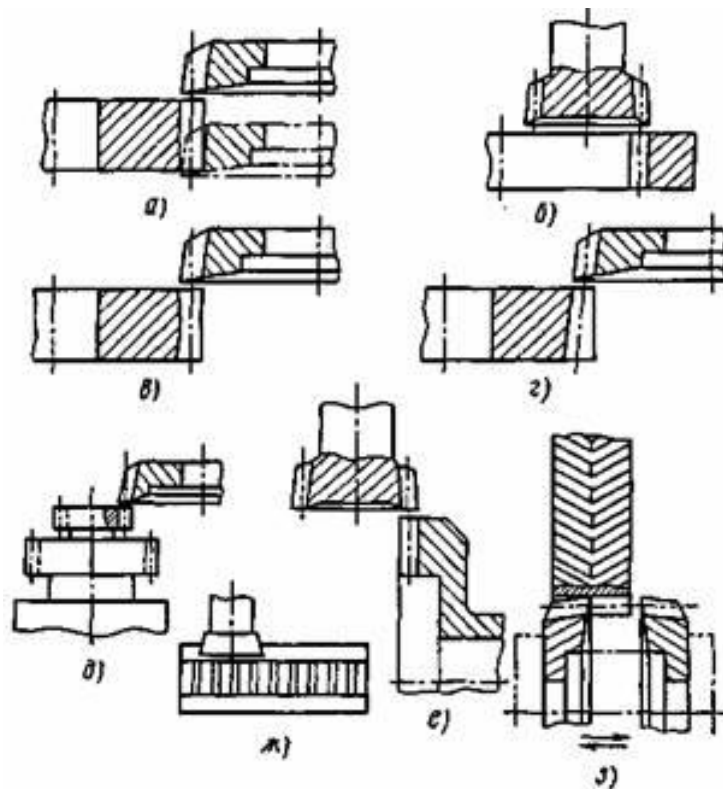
Нарезание зубчатых колес круглыми долбяками на зубодолбежных станках
